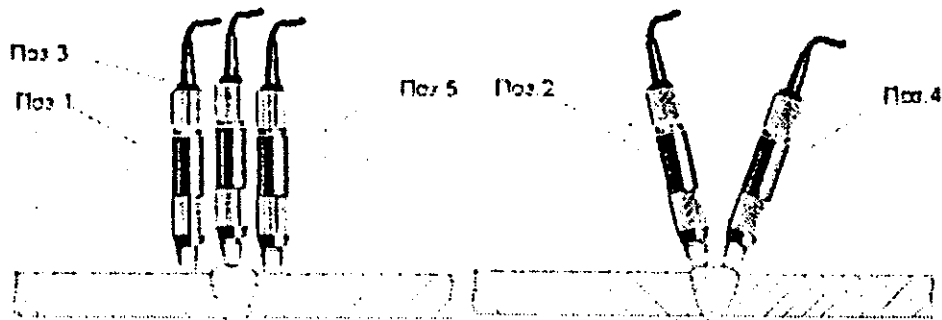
Положение ФП при контроле сварного соединения
